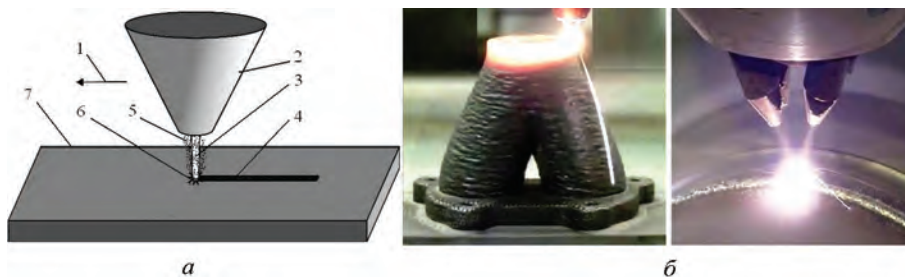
Способ 3D-печати металлоизделий: а – принципиальная схема [9] (1 – направление движения; 2 – сопло осадителя; 3 – пучок лучей лазера; 4 – осажденный слой; 5 – частицы порошка; 6 – зона расплава; 7 – подложка); б – примеры выполнения
